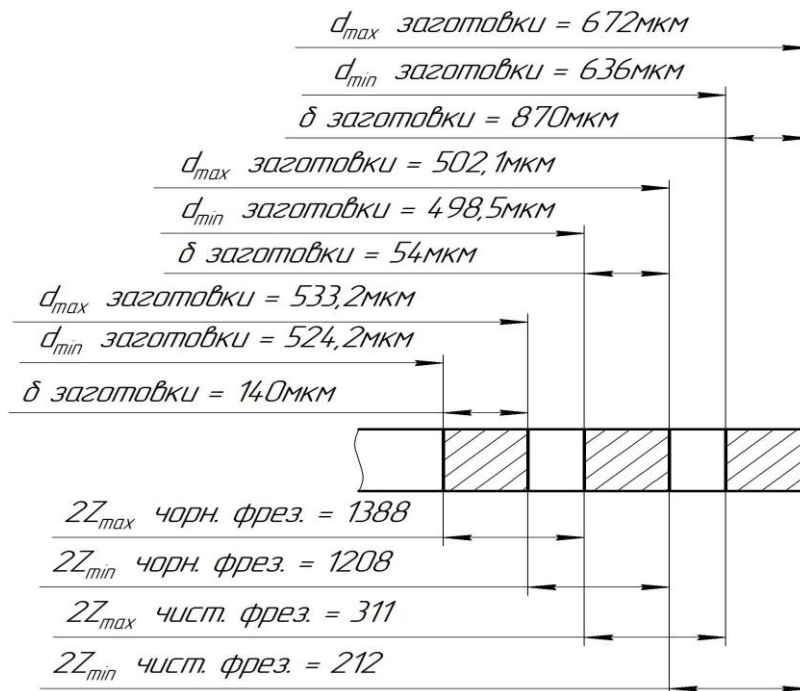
Схема графічного розміщення припусків і допусків на обробку поверхні 100 Н9 деталі сухар.
